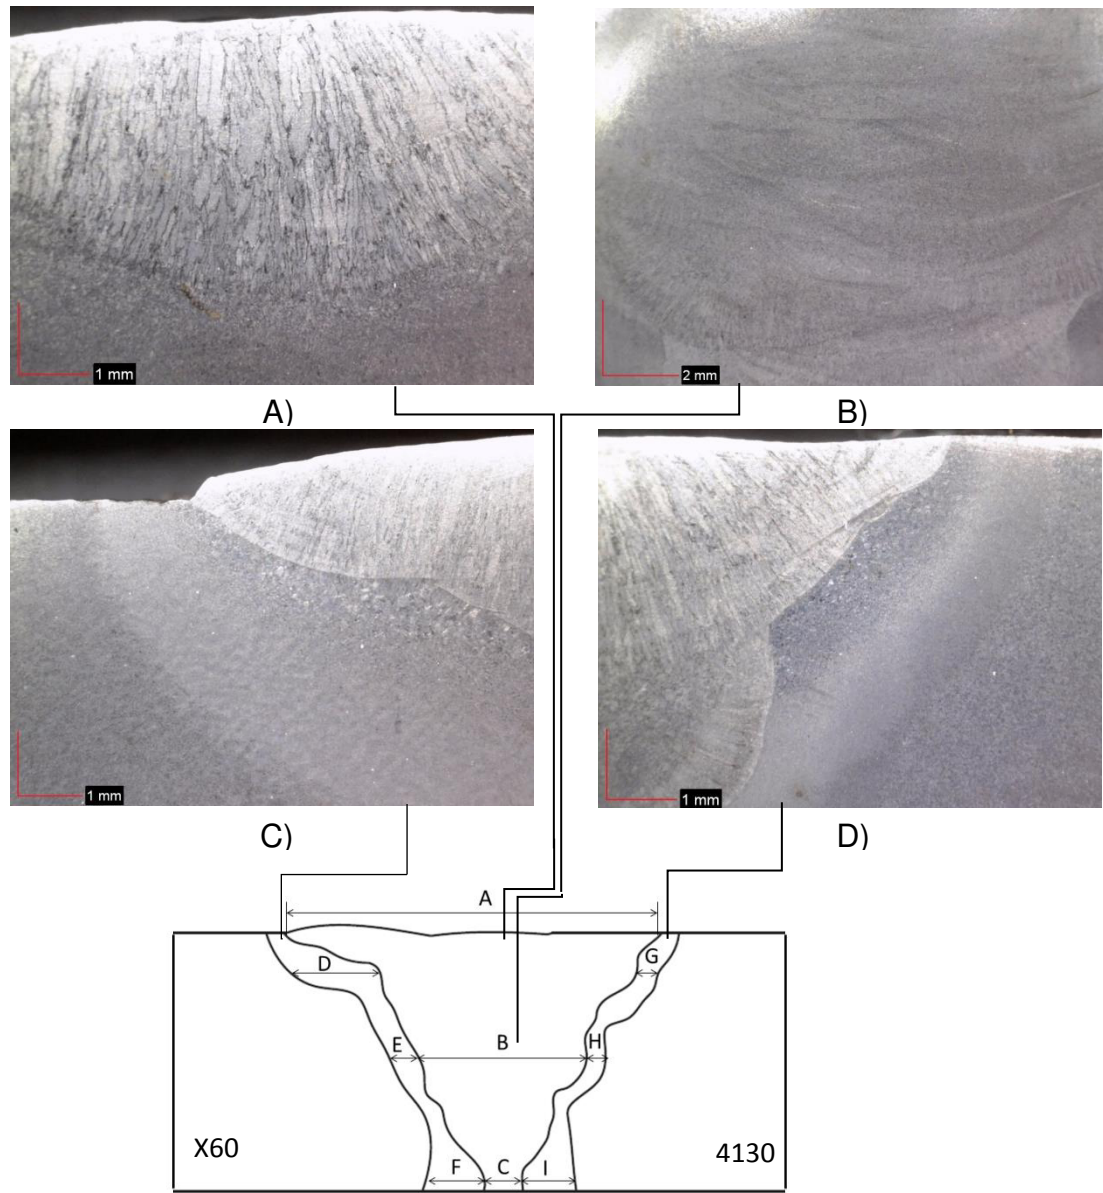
A) Macro estructura de la soldadura cerca de la superficie, B) Macro estructura de la soldadura a medio espesor, C) Macro estructura de la ZAC del X60, D) Macro estructura de la ZAC de la forja.
